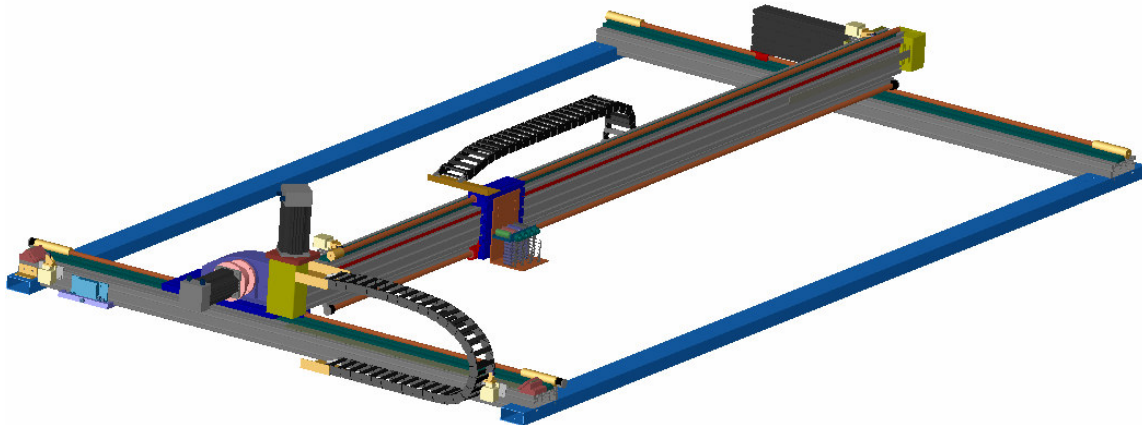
Estrutura mecânica do protótipo do conjunto impressor.
